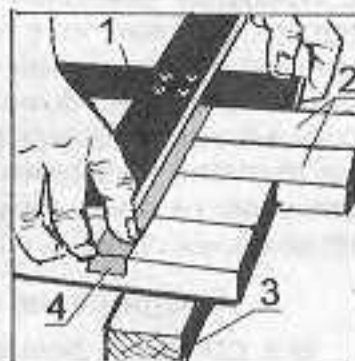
Разметка брусков рамы под обрезку: 1 — крестовина; 2 — бруски; 3 — подставка из бруска; 4 — стяжка из липкой ленты
